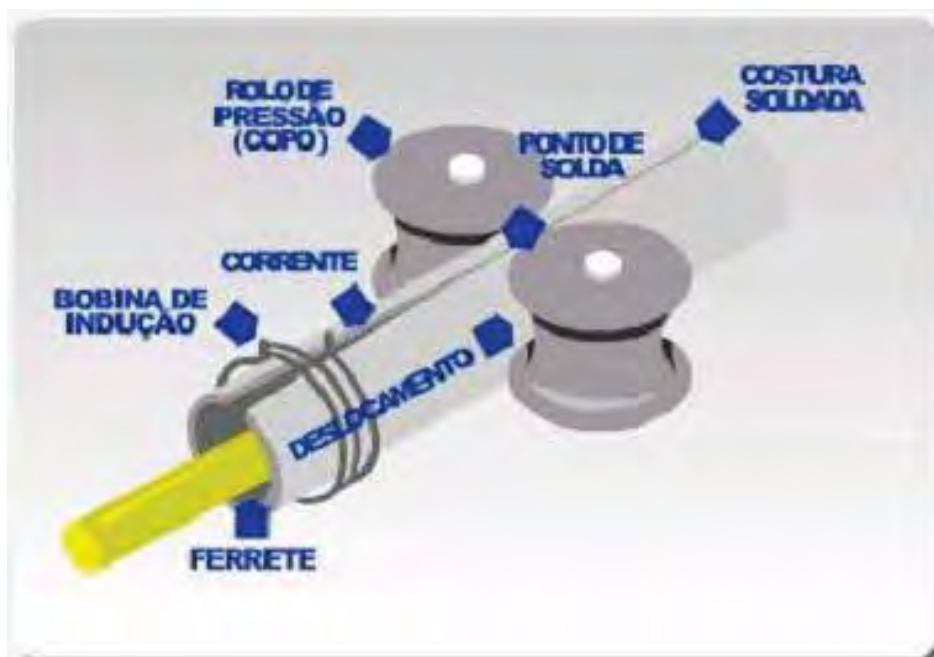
Representação esquemática do processo de soldagem HF/ERW (Cortesia: Tenaris-Confab S.A.).
